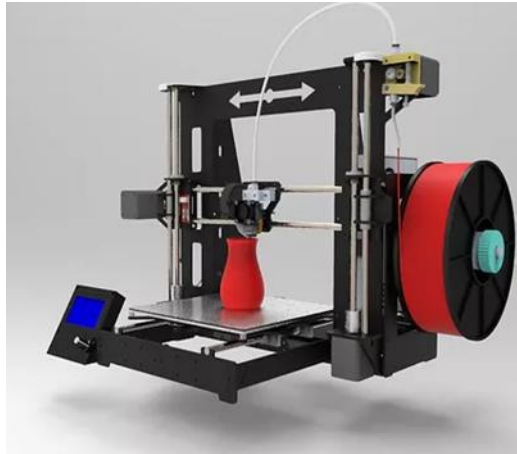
Impresora 3D Deposición de material fundido (FDM) - Fuente: SOTEX
